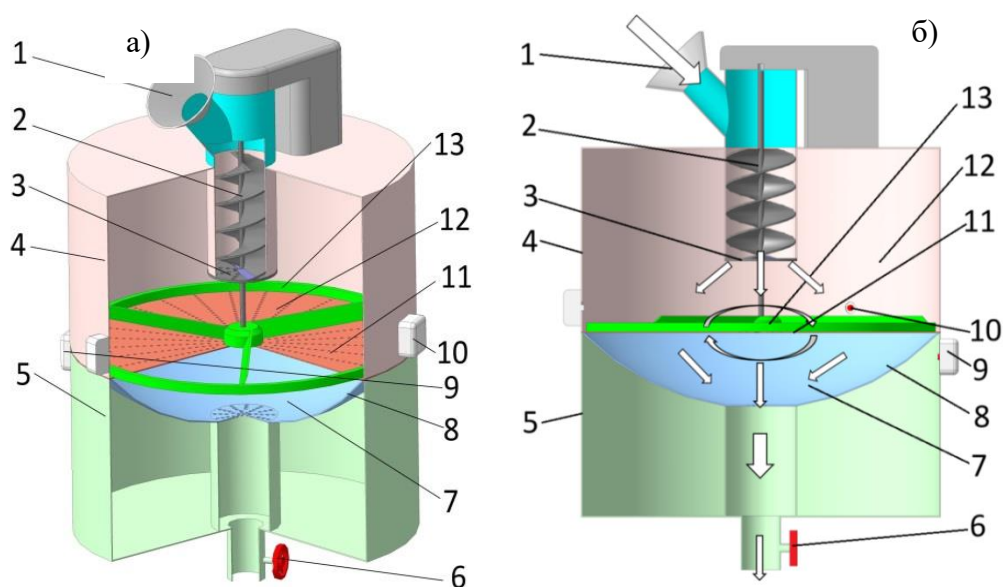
СВЧ-размораживатель с состыкованными тороидальными резонаторами: а) общий вид в разрезе; б) схема протекания технологического процесса; 1 – грузочное устройство, 2 – нагнетательный шнек, 3 – нож с решеткой; 4 – верхний резонатор; 5 – нижний резонатор; 6 – шаровой кран; 7 – конденсаторная часть нижнего резонатора; 8 – диэлектрическая тарелка без дна; 9 – магнетроны на нижнем резонаторе; 10 – магнетроны на верхнем резонаторе; 11 – общее перфорированное основание резонаторов; 12 – конденсаторная часть верхнего резонатора; 13 – диэлектрический перемешивающий механизм
